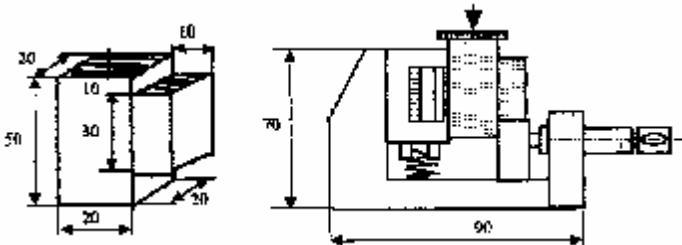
Малый образец для проверки клеящей способности клеев и приспособление для испытания
